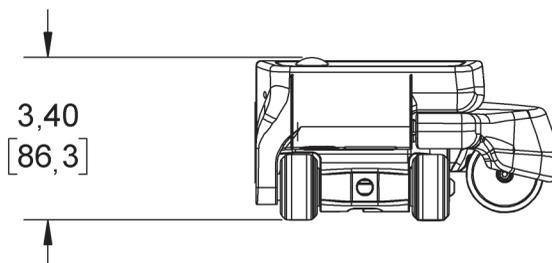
Dimensions sur la vue de face de l'HydroFORM
